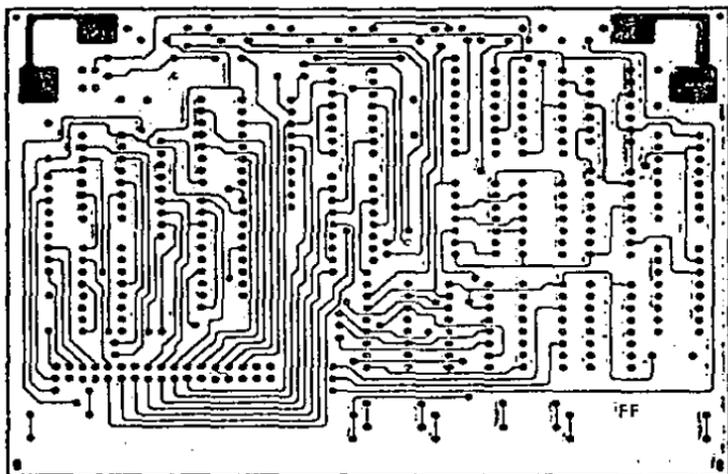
Circuito impreso "principal" lado de componentes.
